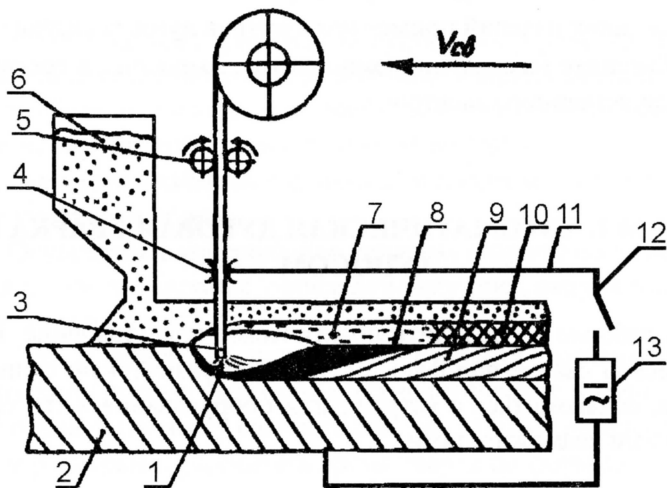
Схема процесса автоматической сварки под флюсом: 1 – электрическая дуга; 2 – заготовка; 3 – электродная проволока; 4 – скользящий токопровод; 5 – механизм подачи; 6 – бункер; 7 – жидкий флюс; 8 – расплавленный металл; 9 – шов; 10 – шлак; 11 – сварочная цепь; 12 – контактор; 13 – источник питания
